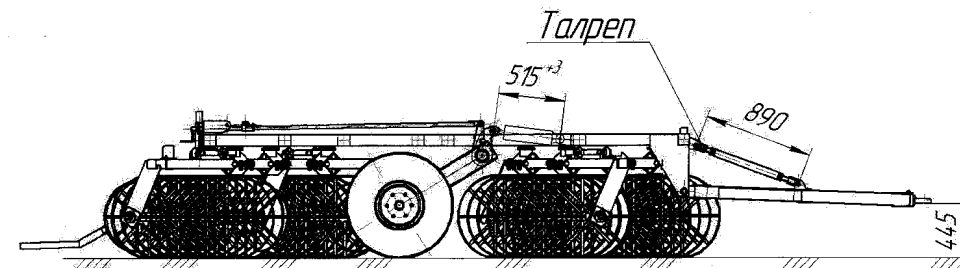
Борона кольцевая модульная «Лидер-БКМ-3,6» (вид сбоку, рабочее положение с регулировкой заглубления)
